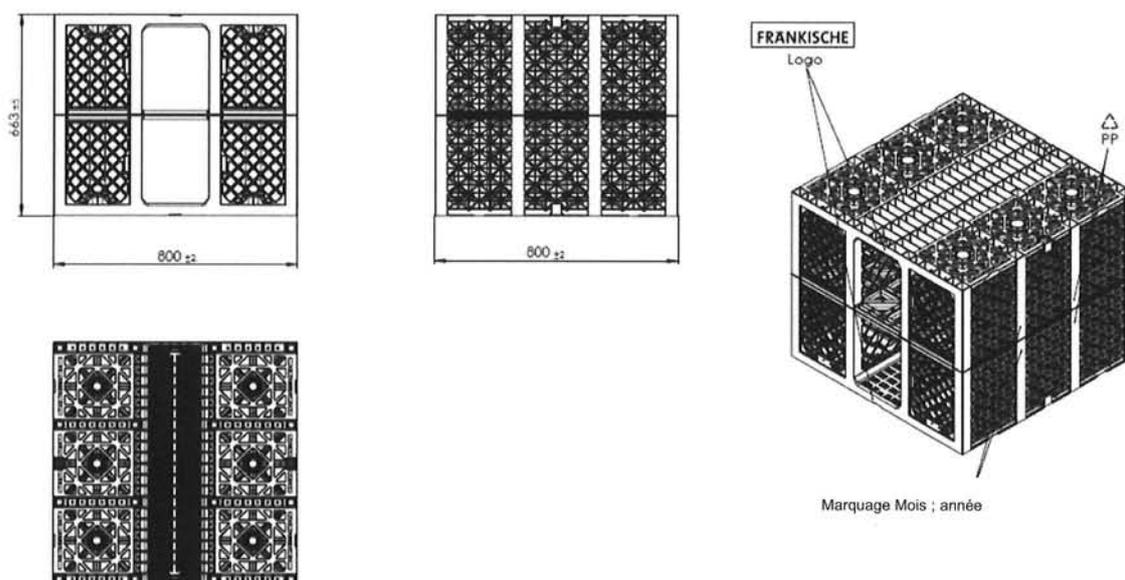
b- Caractéristiques dimensionnelles du module RIGOFILL INSPECT
